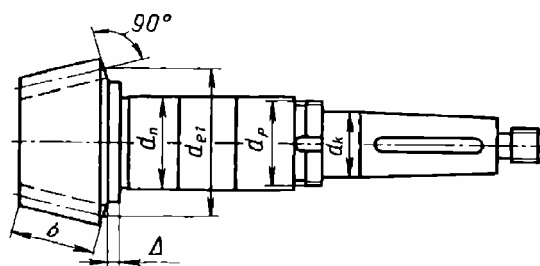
Конструкция вала – шестерни конической зубчатой передачи
